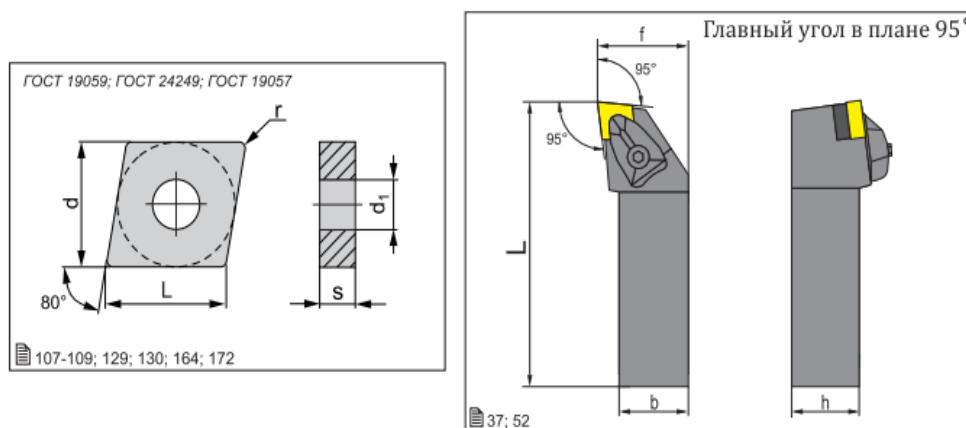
Державка КЗТС DCNLR/L3225 и пластина КЗТС CNMM-190616
